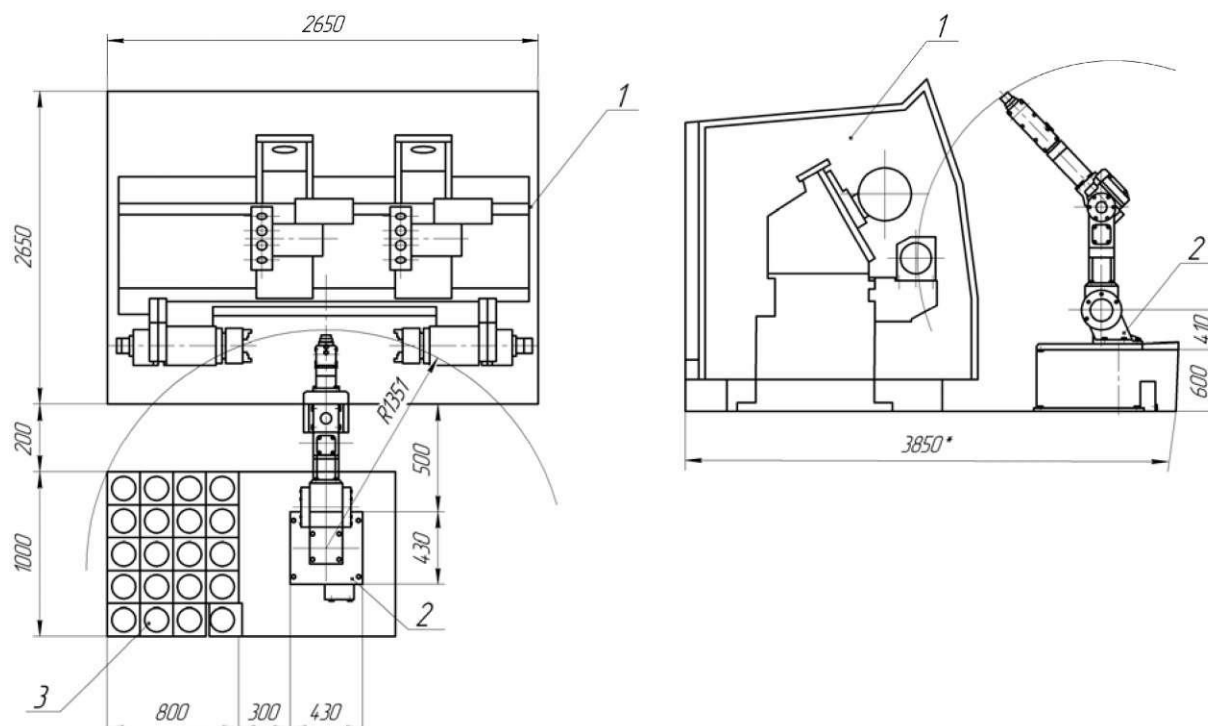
Компонировочная схема РТК на базе ПР напольного типа
